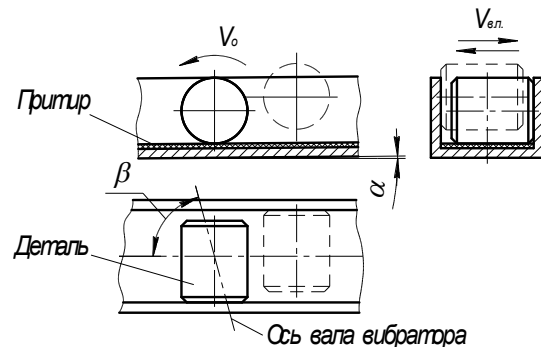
Схема перемещения цилиндрической детали по притиру:
